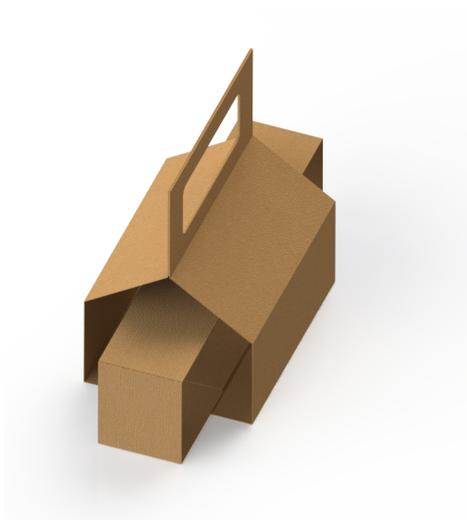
Elemento de transporte plegado. Fuente: Elaboración propia.
